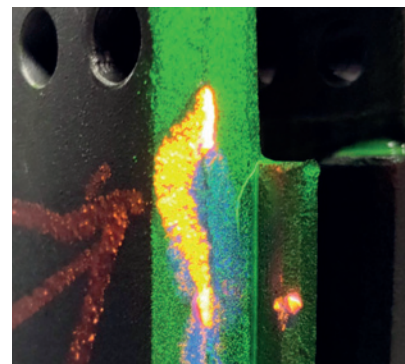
Pęknięcie w narożu wrębu wału wirnika turbiny typu 120 MW
